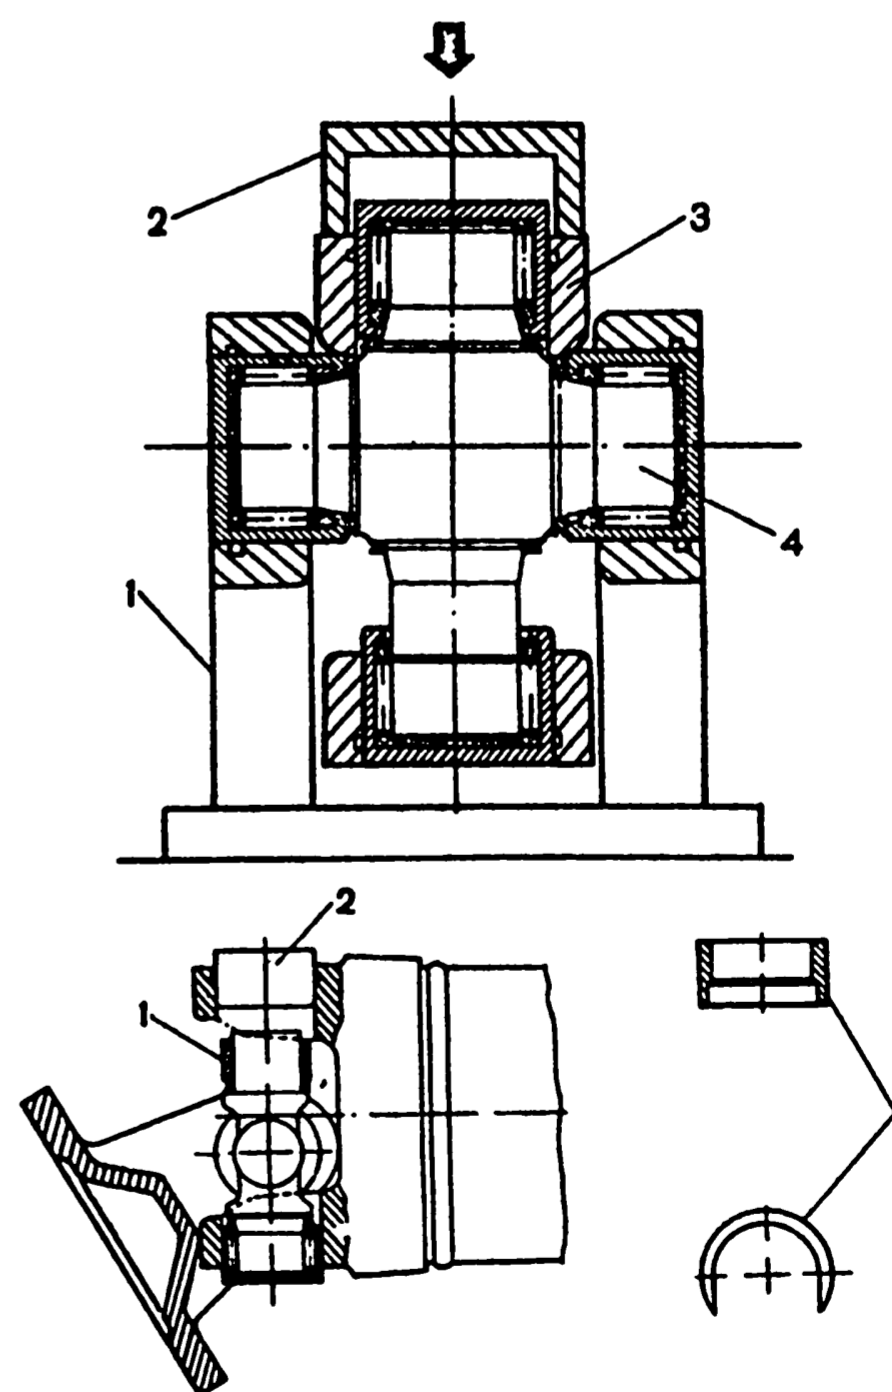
Разборка карданного шарнира (новый конструкции): а) первая операция: 1 - опора прессы; 2 - втулка; 3 - вилка шарнира; 4 - крестовина; б) вторая операция: 1 - разрезная втулка; 2 - подшипник крестовины
